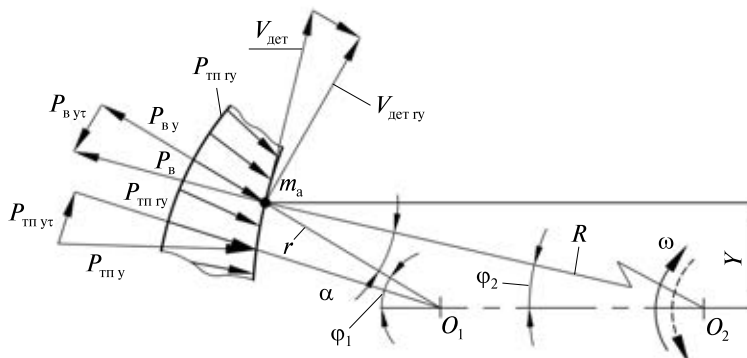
Кінематична схема обробки абразивною часткою поверхні кромки деталі
